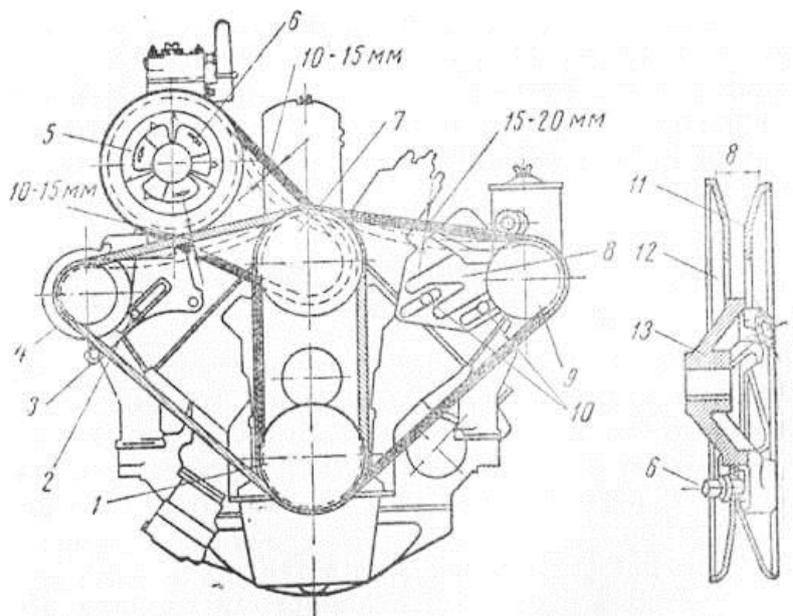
Регулировка натяжения ремней двигателя ЗИЛ-130:
